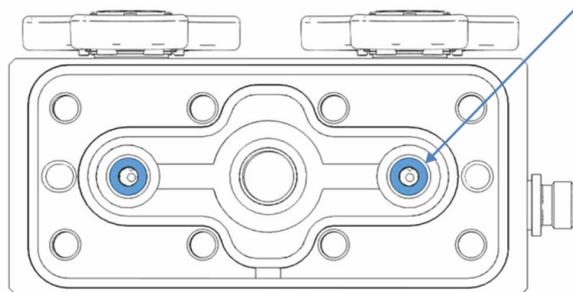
Tête de pompe, joints de piston et bagues de support installés
